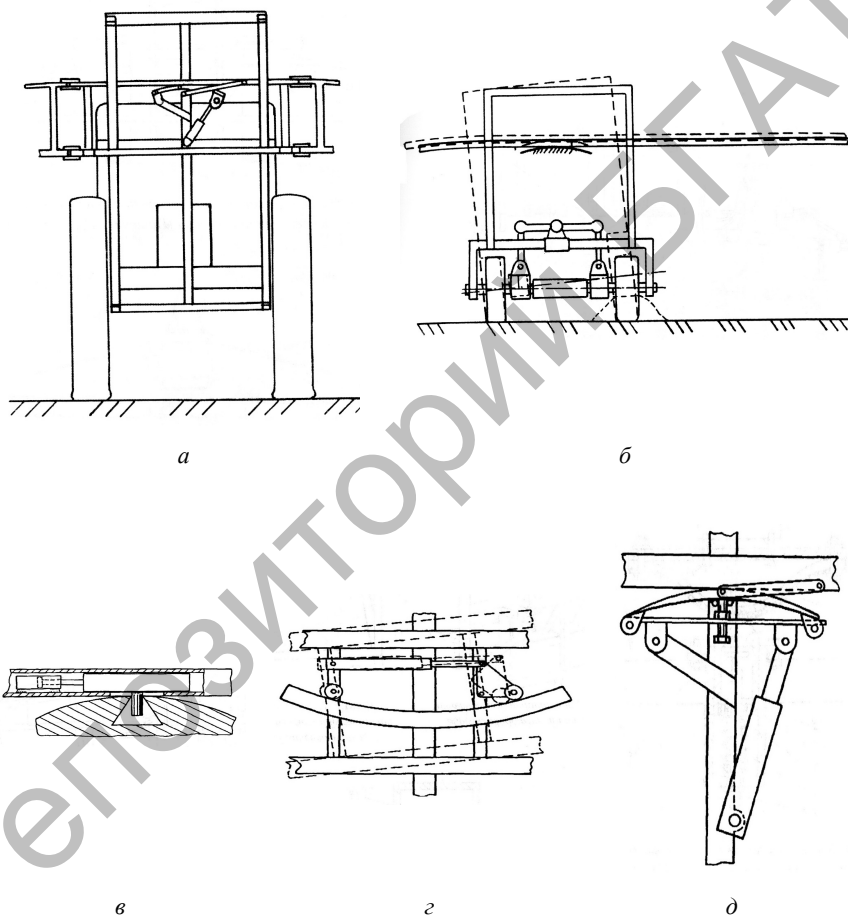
Схемы маятниковых регулируемых подвесок навешиваемых штанг с криволинейными опорными поверхностями (*а, б*) и механизмом изменения угла установки (*в, г, д*) [38]
